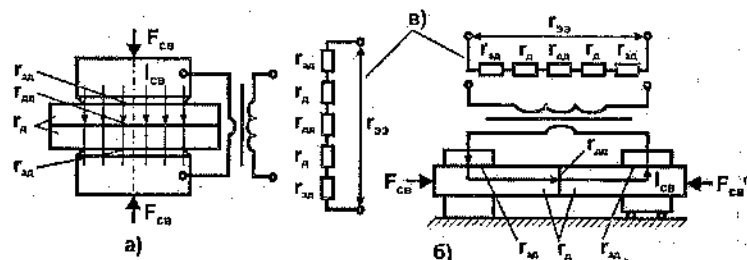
Электрическое сопротивление зоны сварки:
